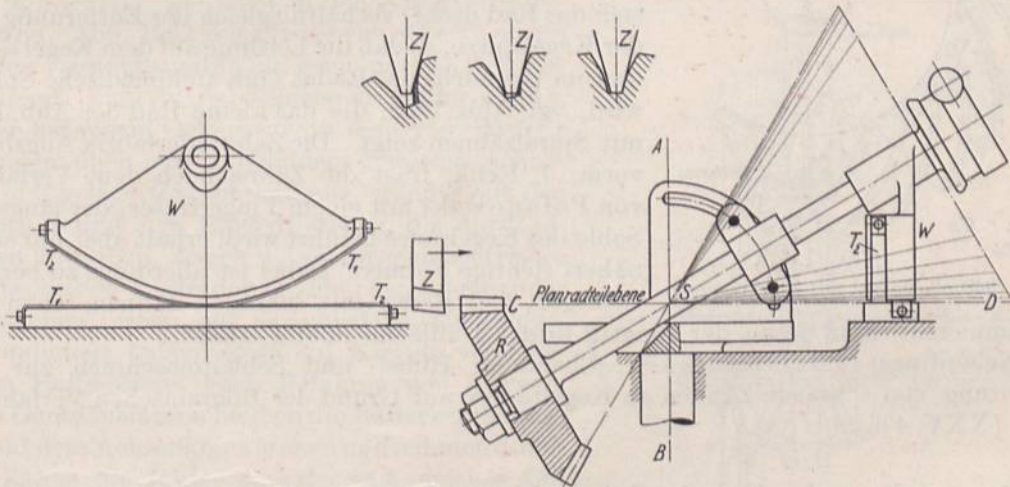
Bilgram-Hobelmaschine zur Bearbeitung von Kegelradzähnen.
